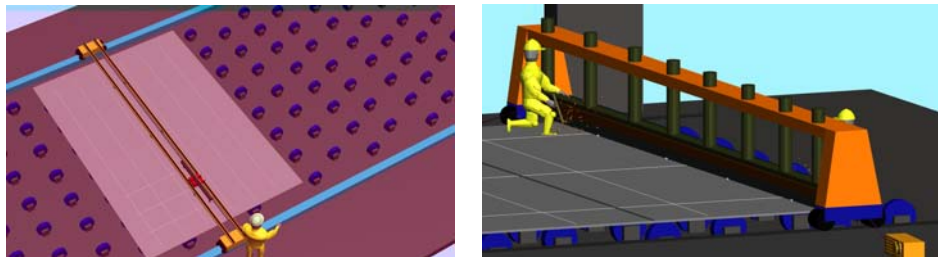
Разметочный агрегат, портал с кассетой для установки
